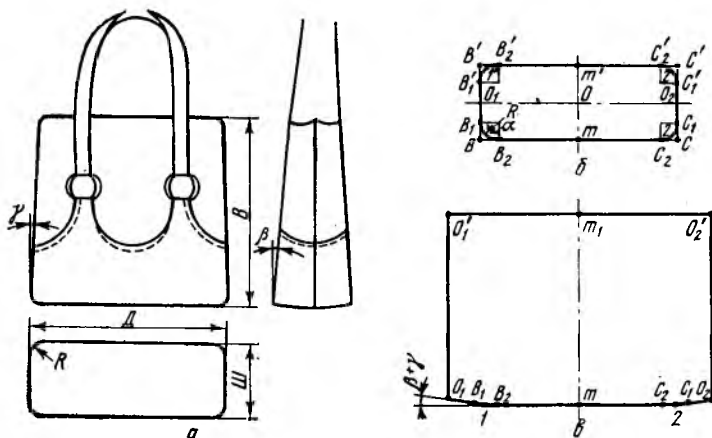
Построение деталей корпуса, состоящего из двух стенок и дна
